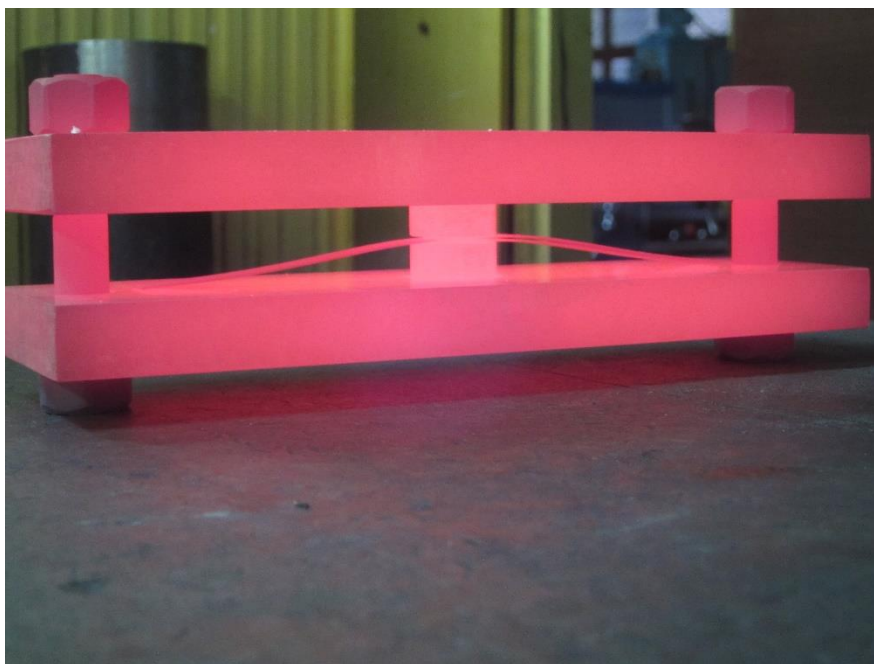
Пристрій з пакетом заготовок при зварюванні в печі
